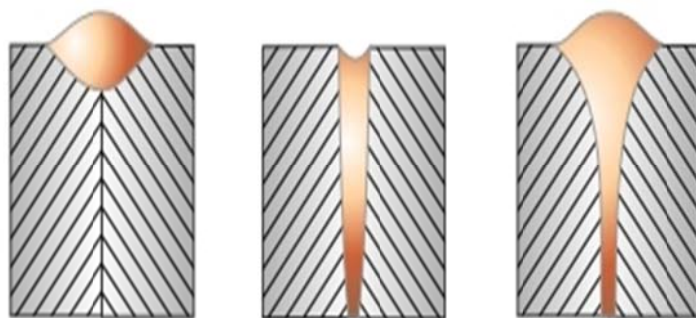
Поперечный разрез шва при дуговой, лазерной, лазерно-дуговой сварке
